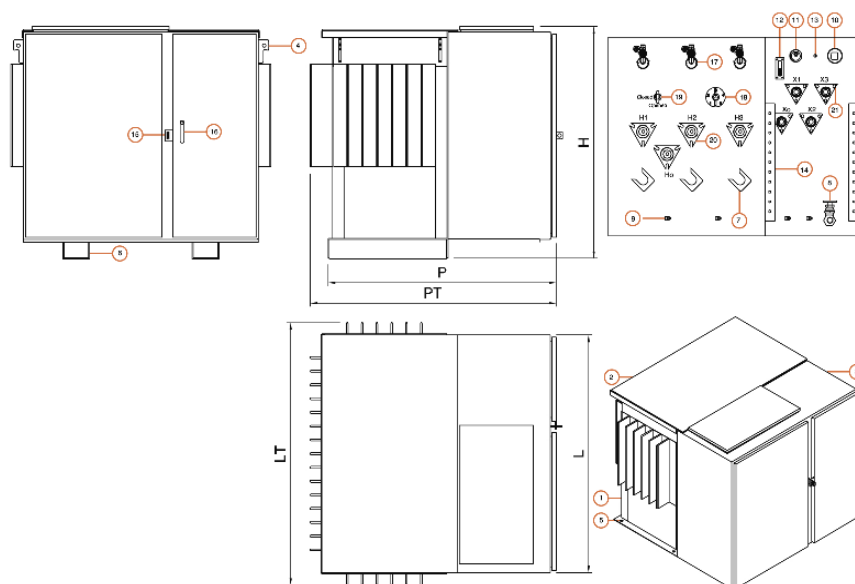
Partes de un transformador trifásico padmounted Tipo Radial
